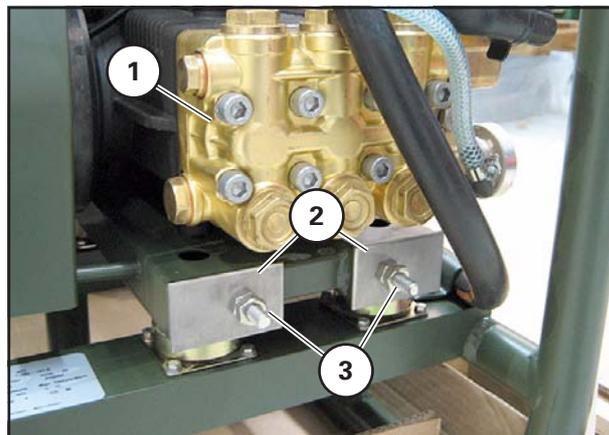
Spannvorrichtung Keilriemen Wasserpumpe
